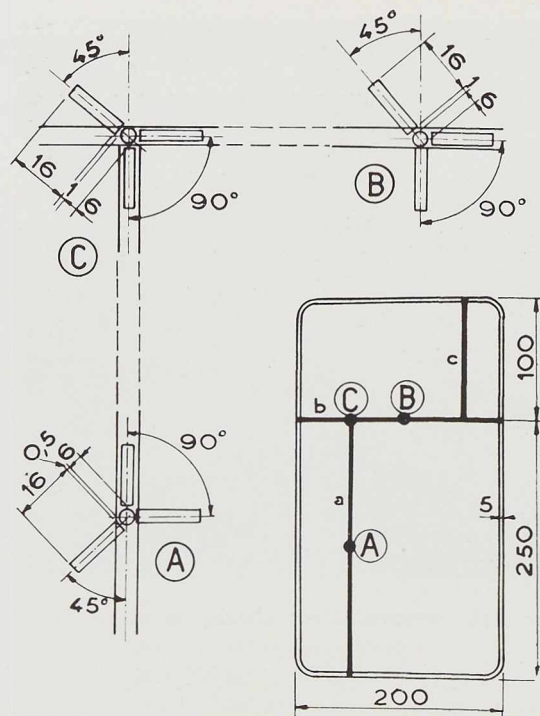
Emplacement et détail des extensomètres sur un réservoir soudé.
